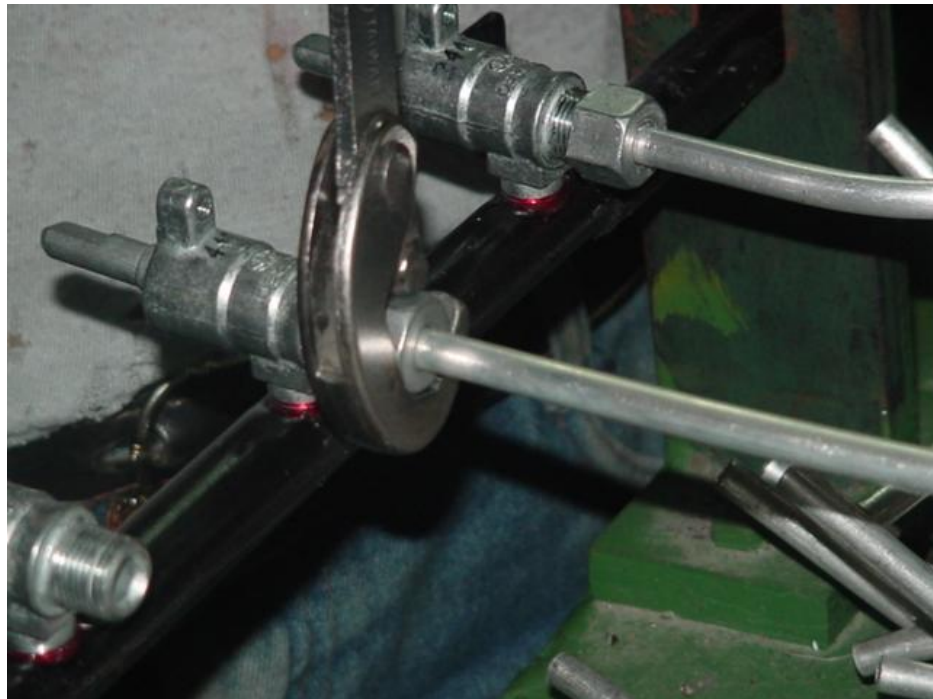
ENSAMBLE DE TUBO DE VALVULAS Y SOPORTE CON TUBERIA DE ALUMINIO.
